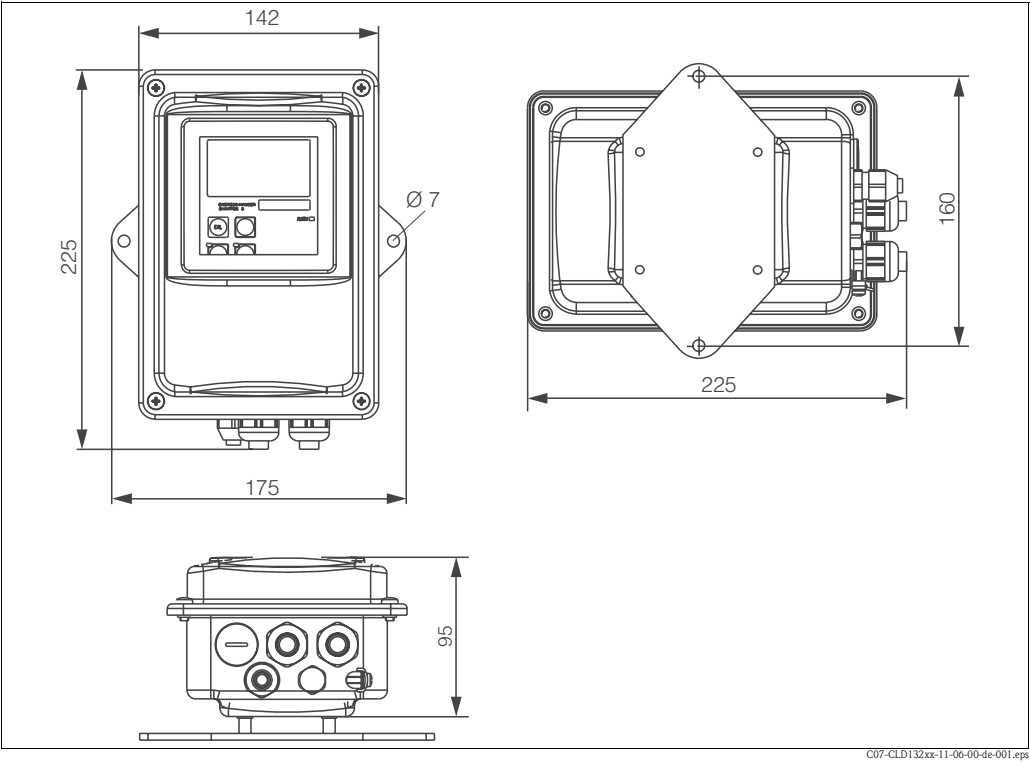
CLD132 pour montage mural avec plaque de montage
